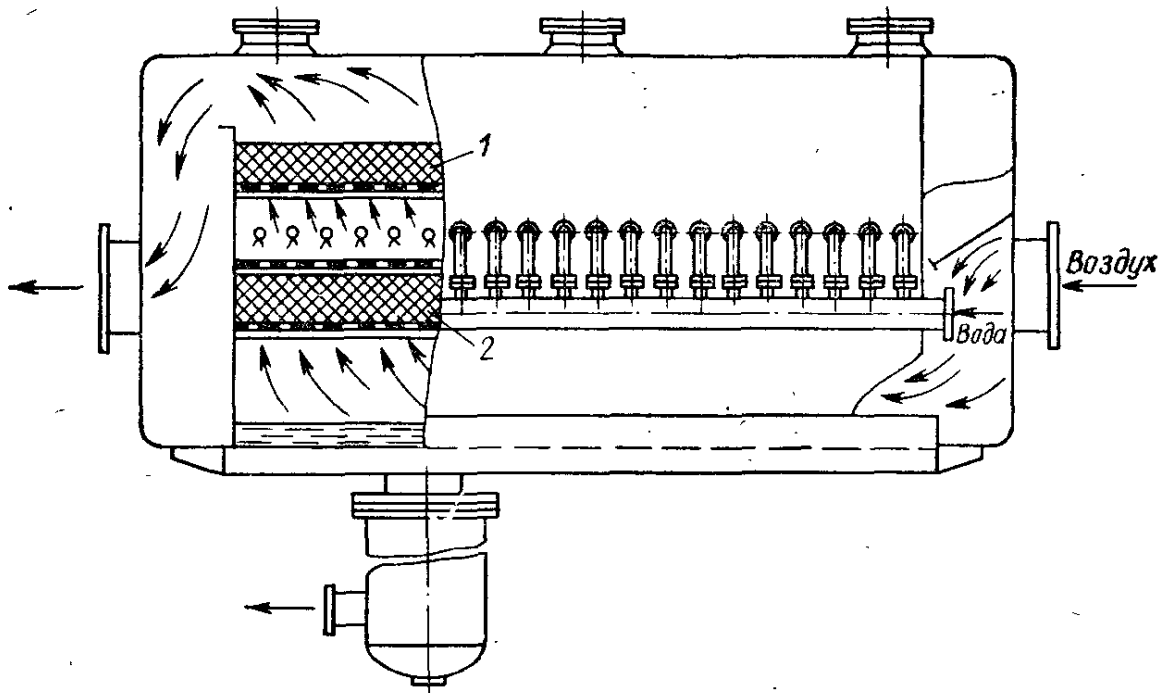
Повітреохолоджувач із зрошувальною насадкою
